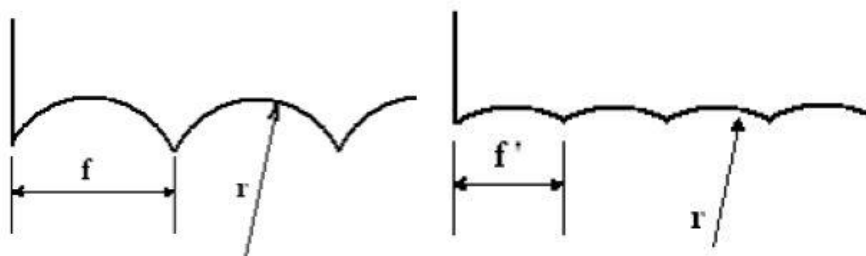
3 – Superfície usinada com avanço f , f' e raio de ponte r (Fonte: SANCHES, 2011).
